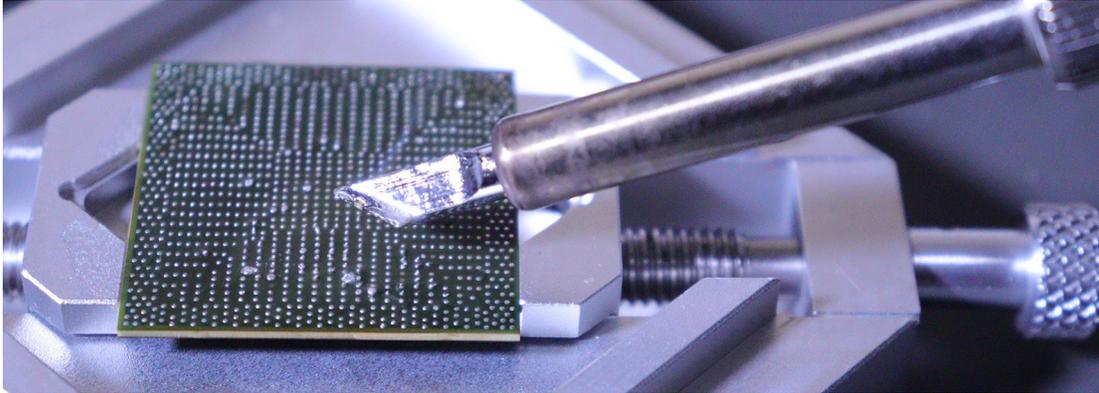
remoção do excesso de solda com o ferro de soldar e ponteira do tipo faca
